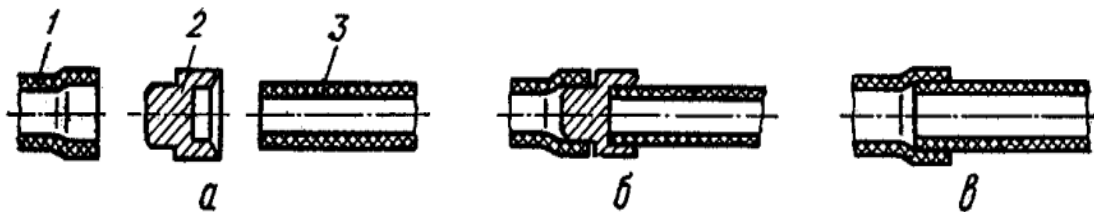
Зварювання врозтруб: а-початкове положення; б-оплавлення; в-готовий виріб. 1,3-труби; 2-нагрівний інструмент.
